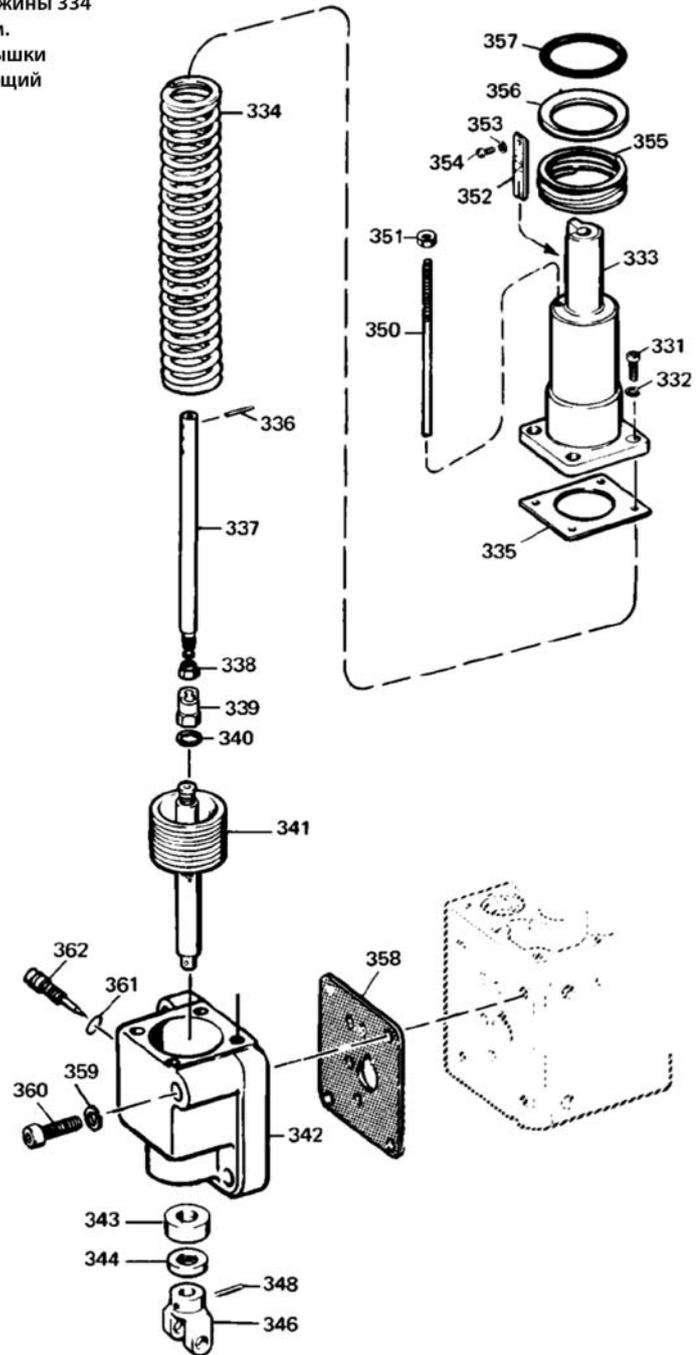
Покомпонентный чертеж подпружиненного силового цилиндра (16 Дж) с поступательным выходом
